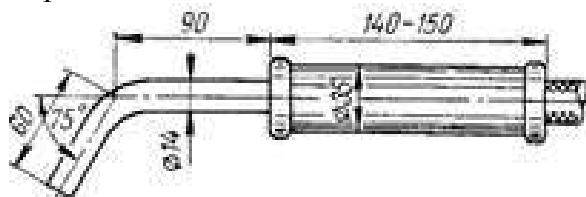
Электрододержатель для безогарковой сварки
